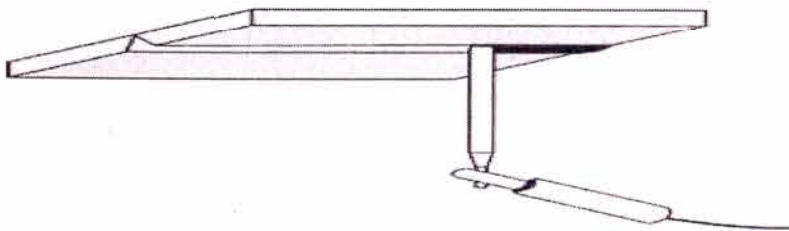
Soldadura: Posición Sobrecabeza
